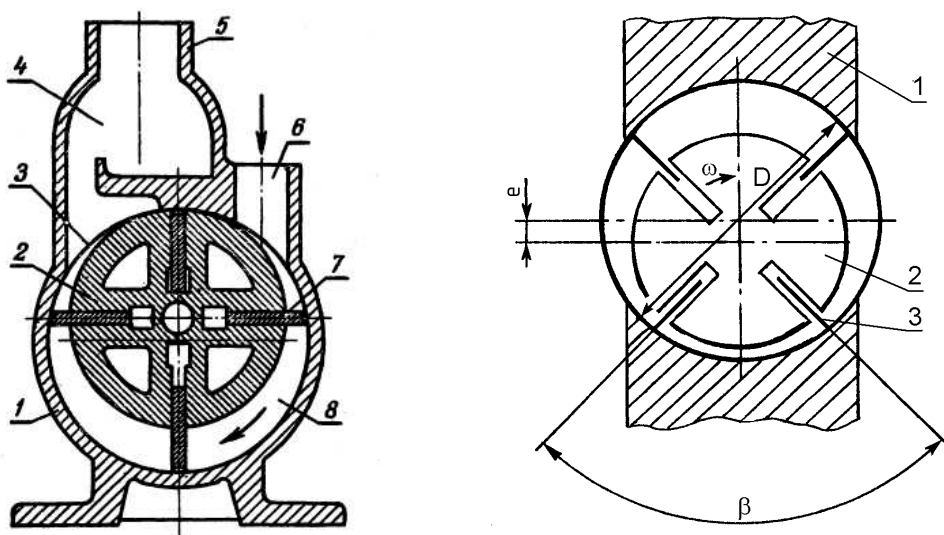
Схема ротаційного лопатевого вакуумного насоса: 1 – корпус; 2 – ротор; 3 – бічні прорізи; 4 – верхня камера; 5 – випускна труба; 6 – впускна труба; 7 – пластини; 8 – бічна камера.
